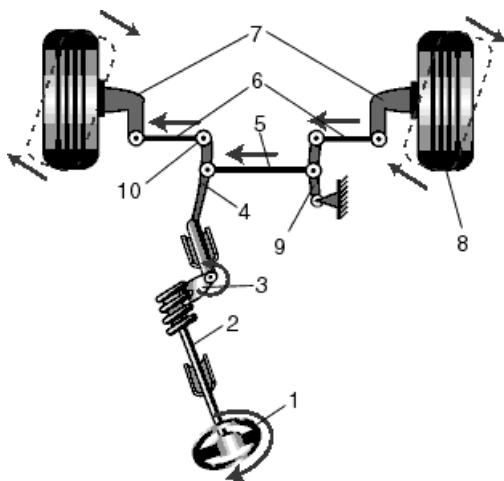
Схема рулевого управления с механизмом типа «червяк-ролик» 1 - рулевое колесо; 2 - рулевой вал с «червяком»; 3 – «ролик» с валом сошки; 4 - рулевая сошка; 5 - средняя тяга; 6 - боковые тяги; 7 - поворотные рычаги; 8 - передние колеса автомобиля; 9 - маятниковый рычаг; 10 - шарниры рулевых тяг
